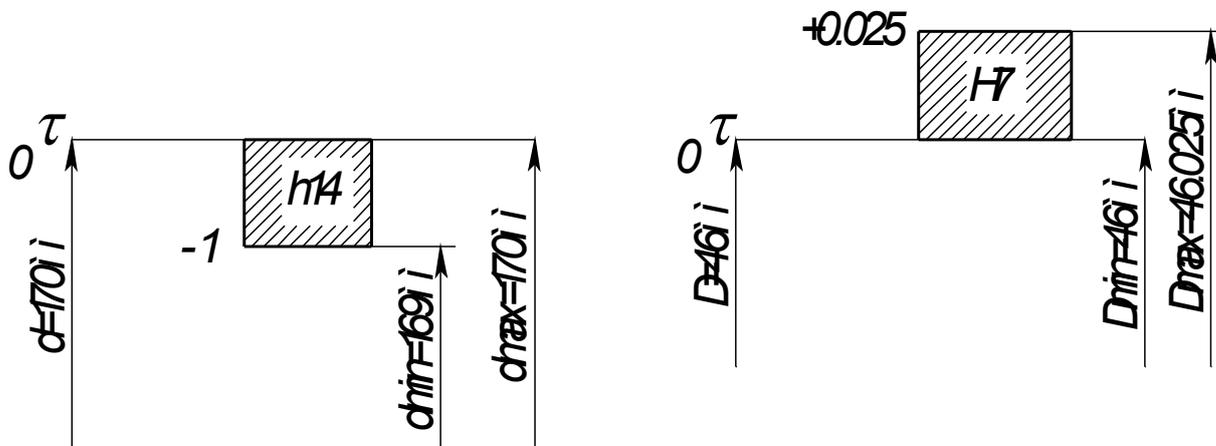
,1 – схемы расположения полей допусков на размеры:
